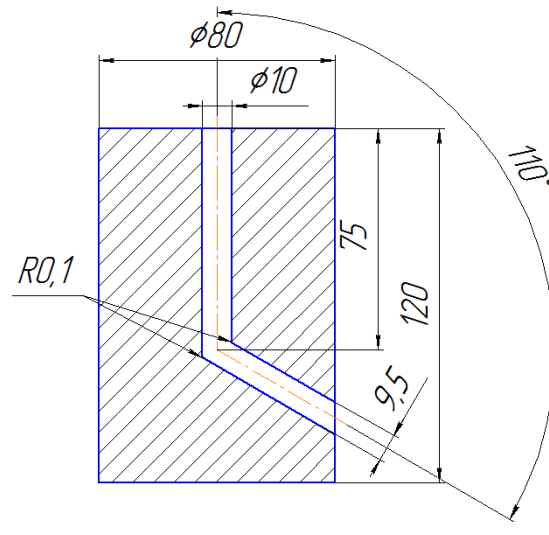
Форма и размеры матрицы для углового прессования цилиндрических заготовок
